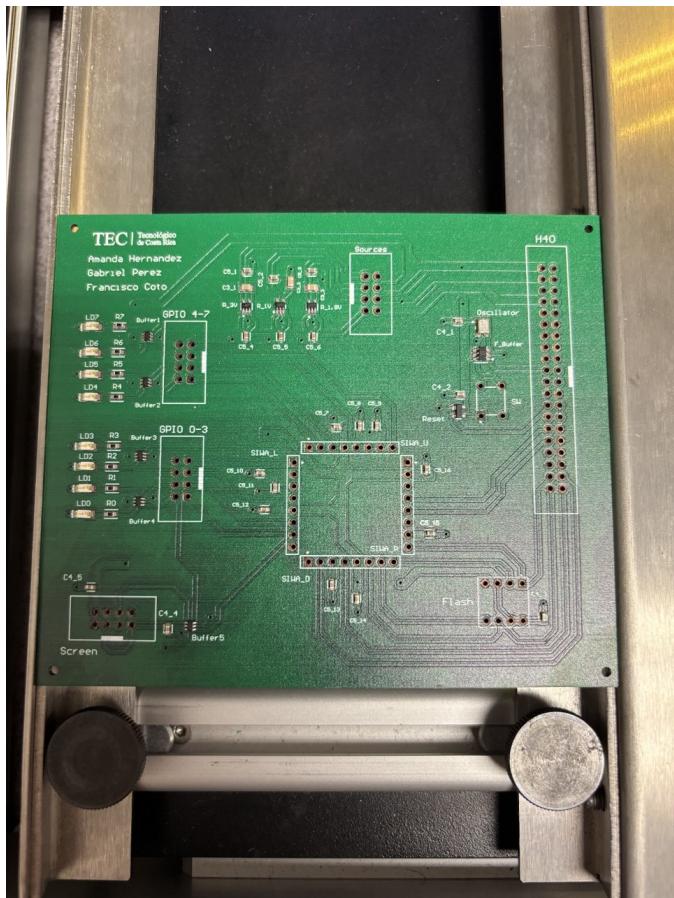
PCB luego ensamblar componentes de montaje superficial.
